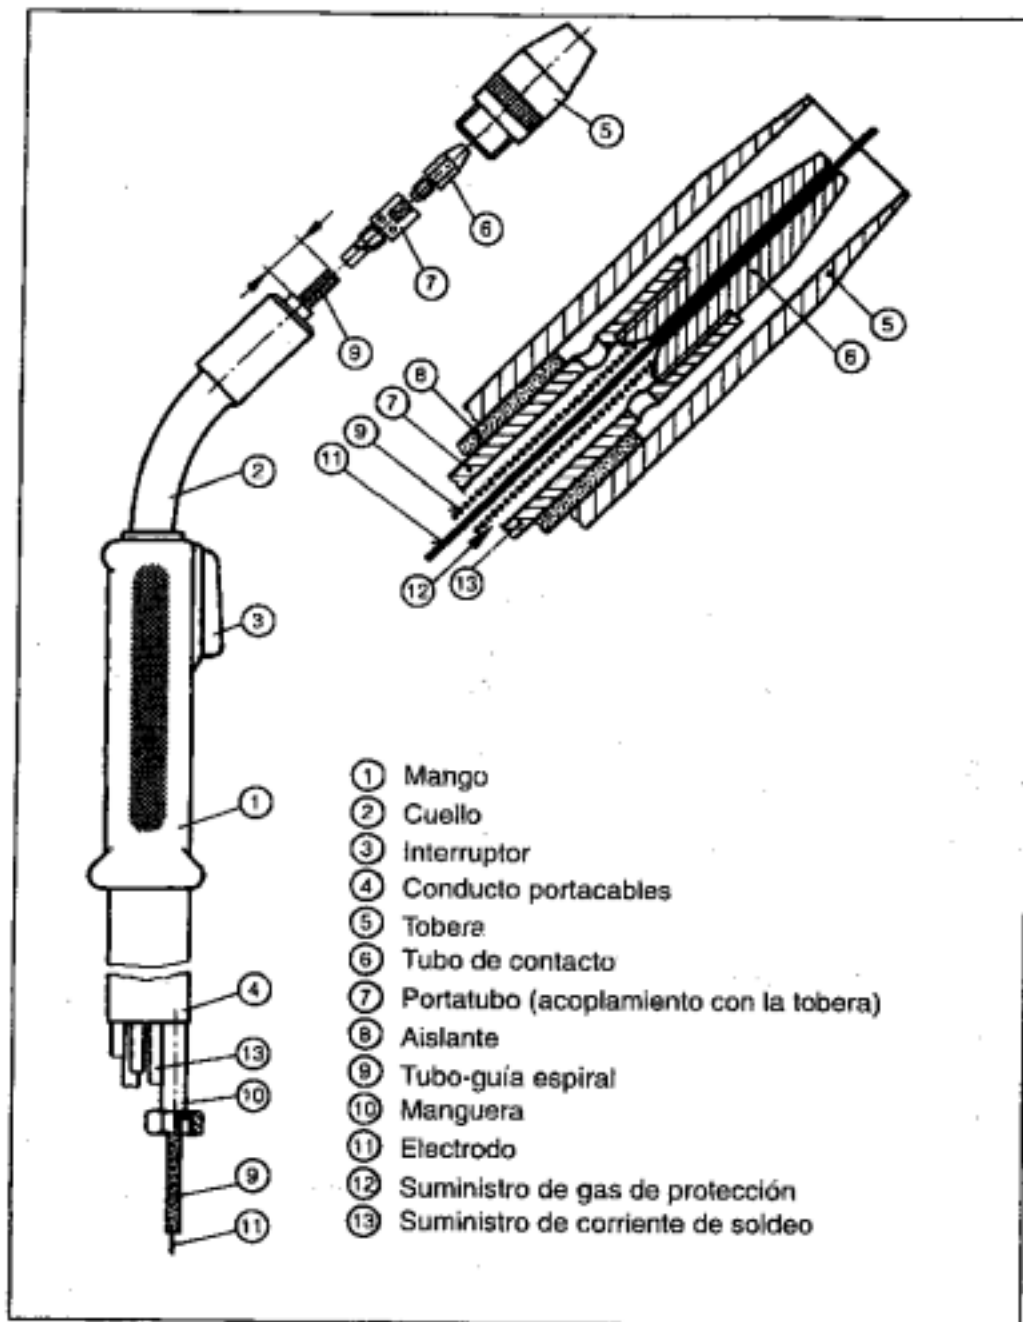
PISTOLA PARA EL SOLDEO MIG/MAG (ACERO AL CARBONO)
